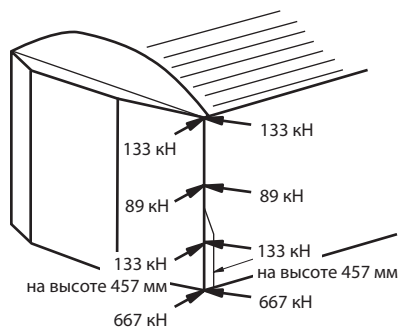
Нормированные нагрузки на угловые конструкции кузова
